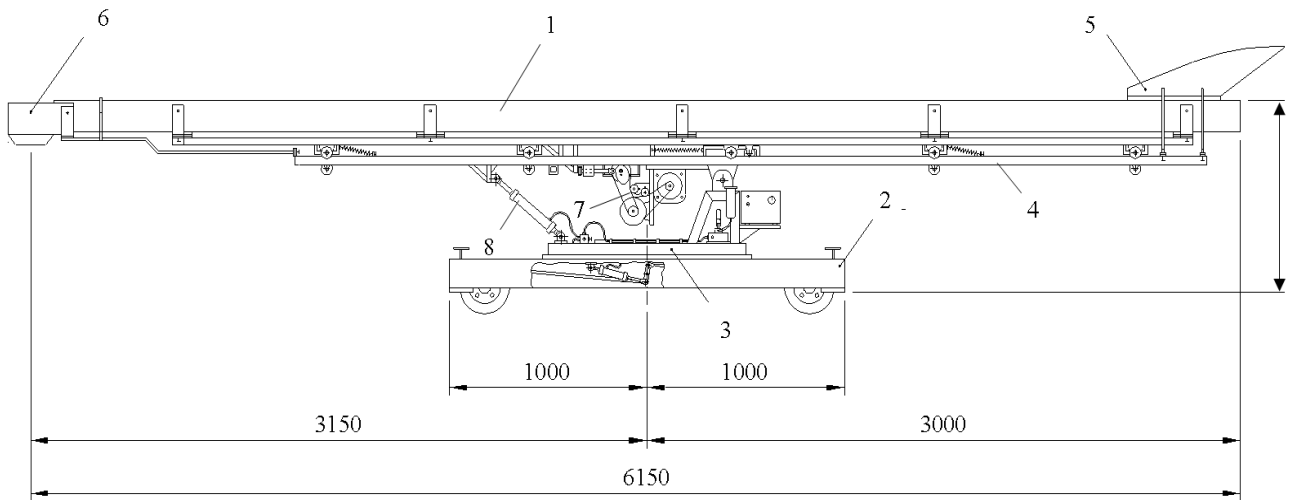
Конструктивная схема переставного инерционного конвейера для подачи бетонной смеси к месту укладки:
